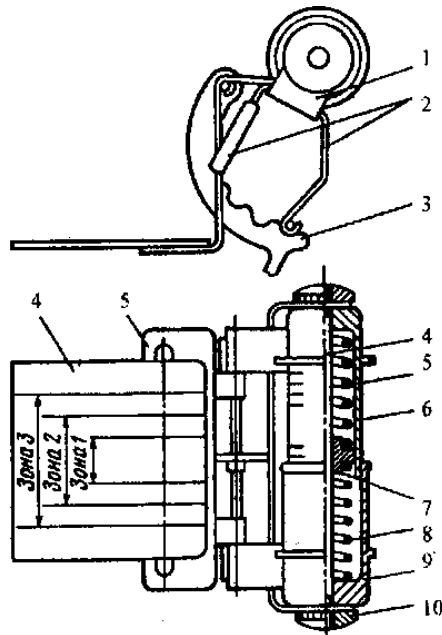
Прибор К-178 для перевірки рульового керування
